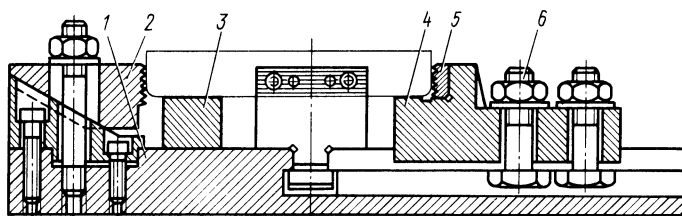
Универсальное приспособление для фрезерования деталей типа крышек и планок
